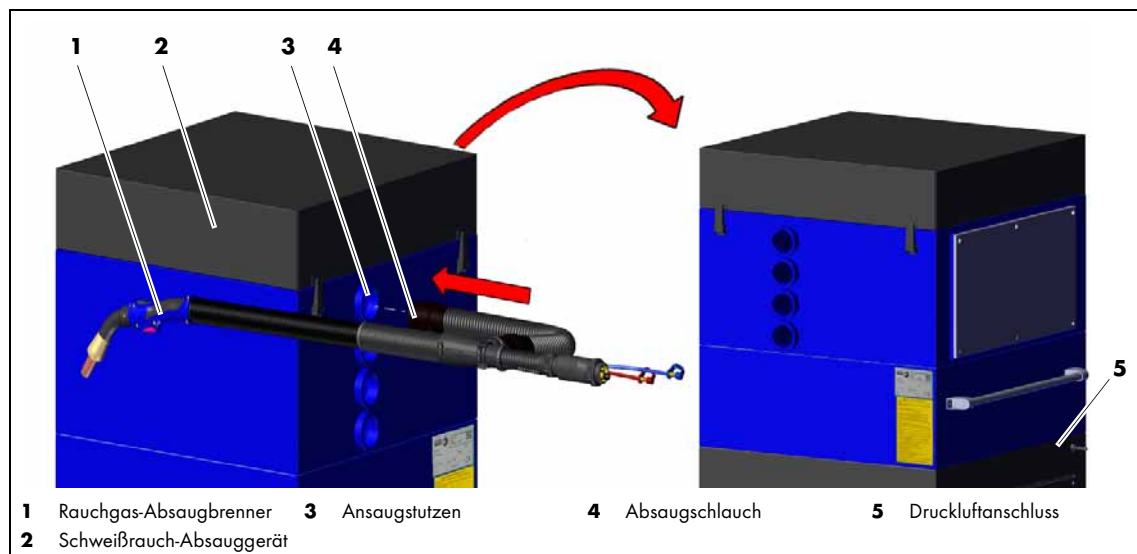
Absaugschlauch des Schweißbrenners montieren
